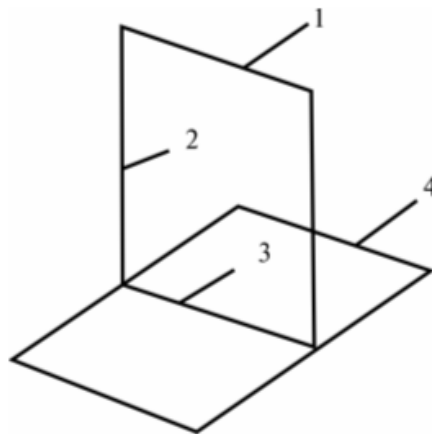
Схема каркаса кабіни. 1 – верхня балка; 2 – стійка;
